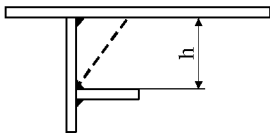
Схема расчетных сечений сварного соединения с угловым швом
